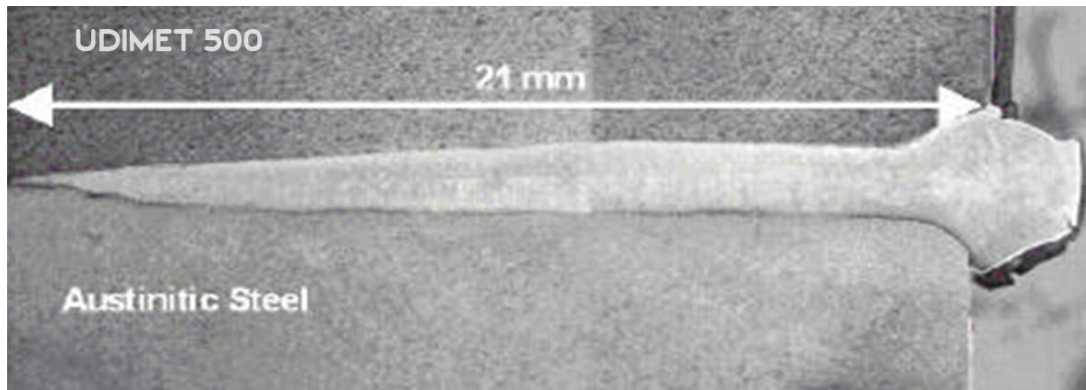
L'exemple d'un EB a soudé le disque du compresseur UDIMET-500 (dessus) jointif à un disque austénitique d'acier inoxydable.
